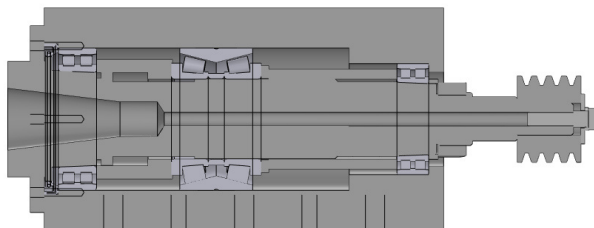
Общий вид шпиндельного узла (модель) оборудования для механической обработки стыковых поверхностей резиноканевых конвейерных лент
